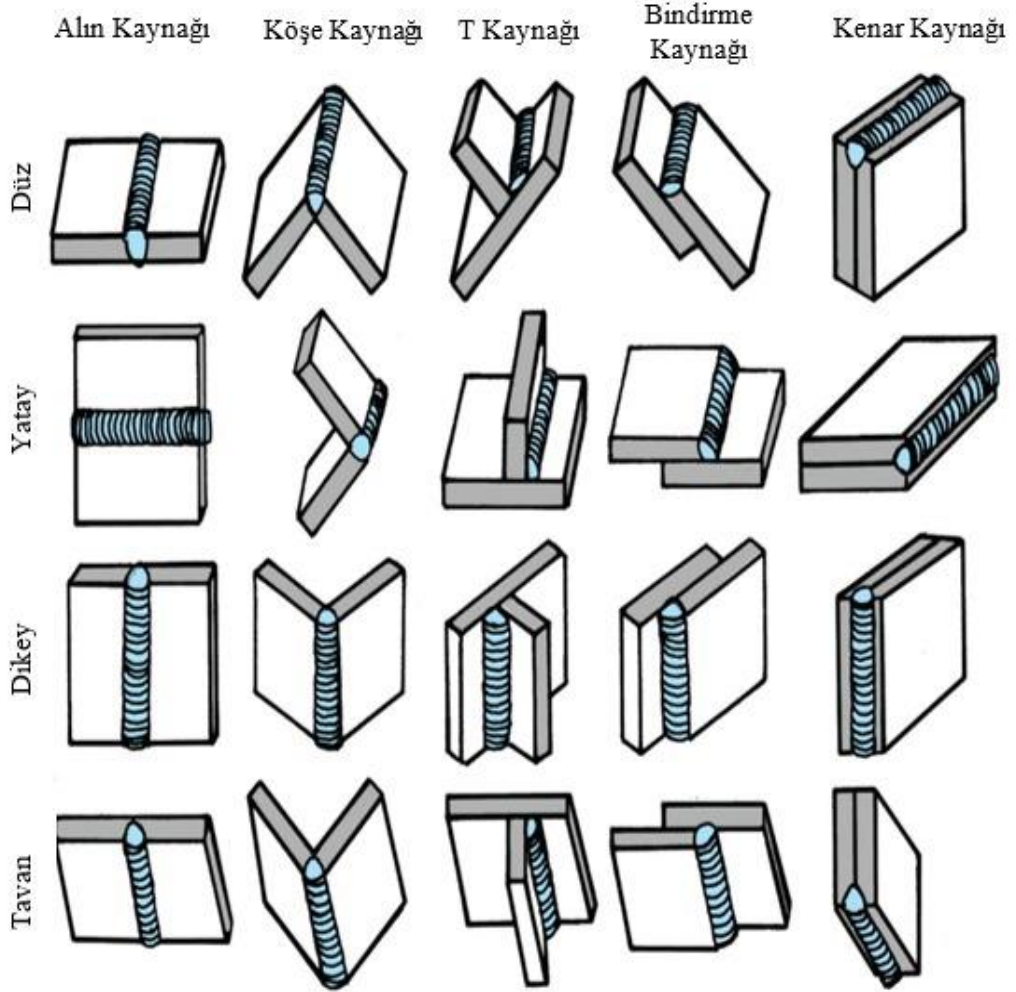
Kaynağın sınıflandırılması (American Welding Society).
